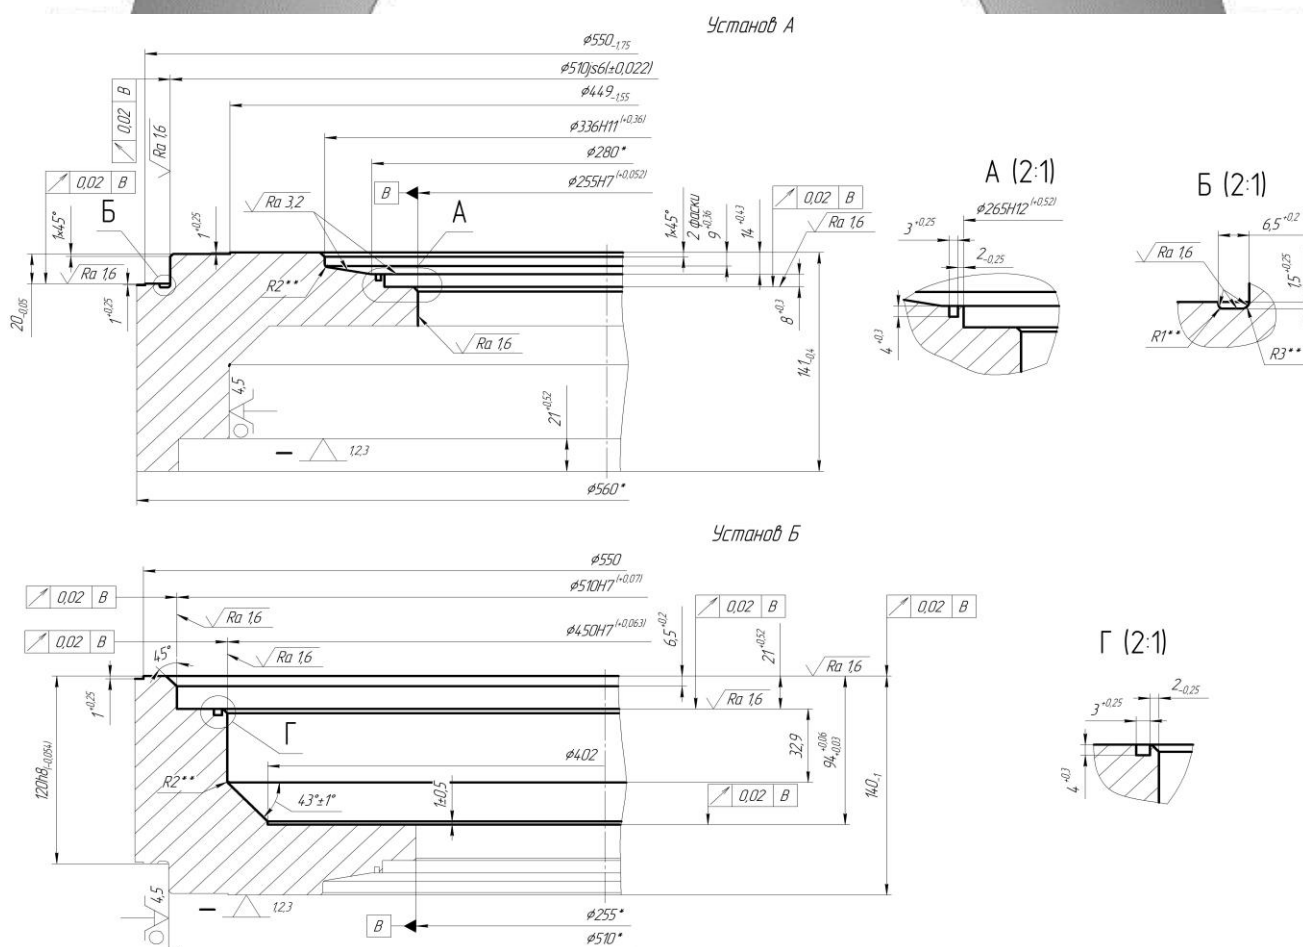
Схема базування заготовки на токарній операції (перший варіант)
